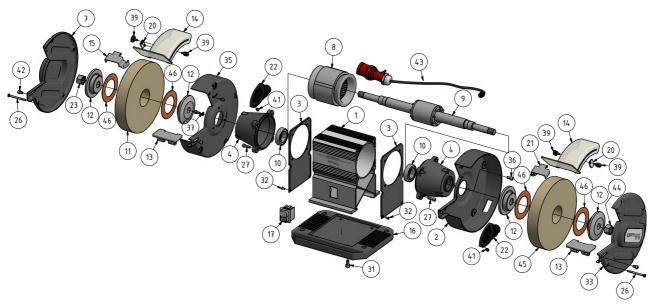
Ersatzteilzeichnung - Spare parts drawing
